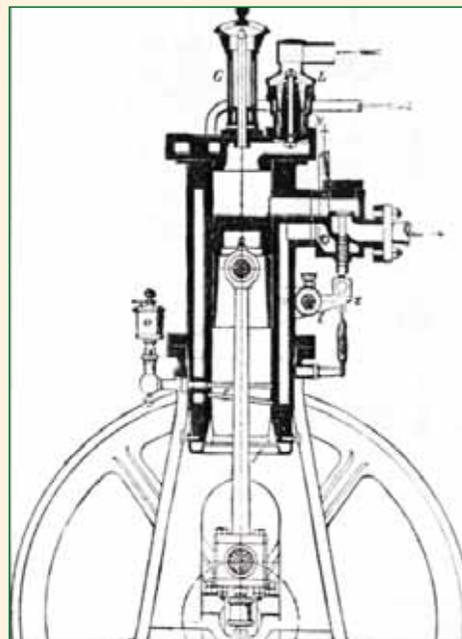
"Безопасный" двигатель Б.Г. Луцкого (рисунок взят из книги Ф. Засса): а, b, с - трубопровод подачи бензина; d - впускной клапан; e - отверстия для подачи бензина к воздуху; f - калильная трубка; g - подогрев калильной трубки; h - трубопровод подачи воздуха; i - трубопровод подачи охлаждающей воды; k - выпускной клапан
